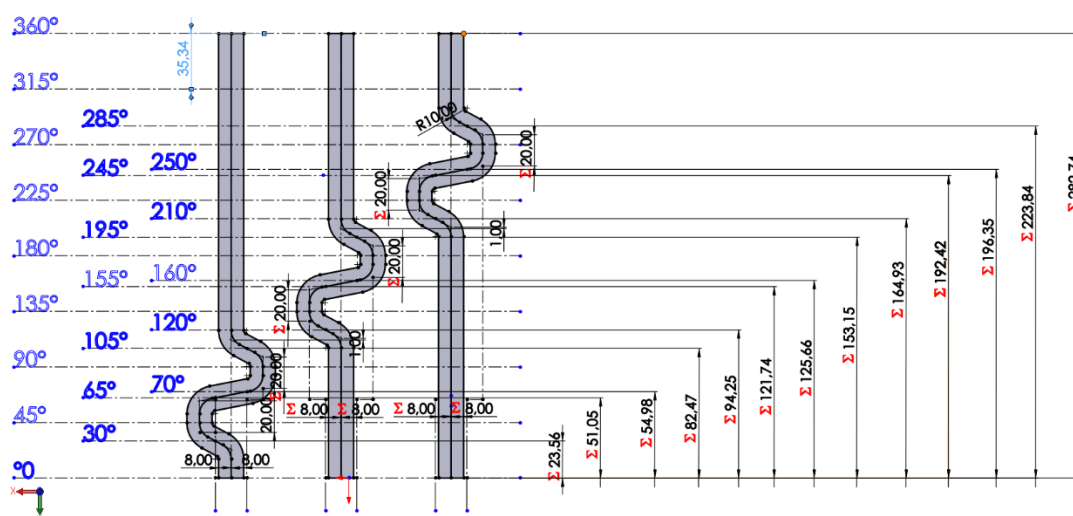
páka SEQSHIFT [105] Obrázek 5-42 Modifikace páky řazení [105]
